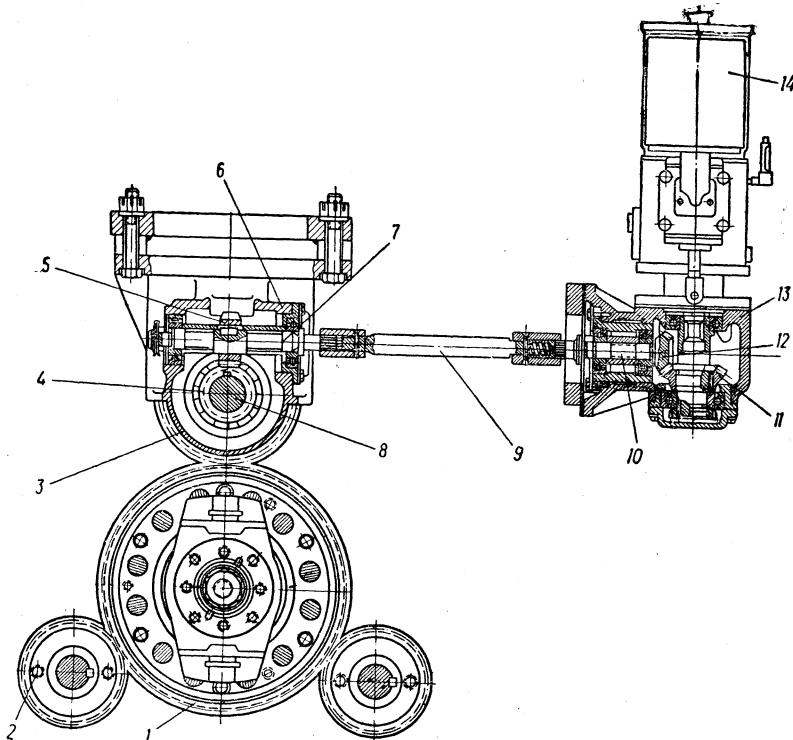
Привод регулятора числа оборотов дизеля 2Д100:
